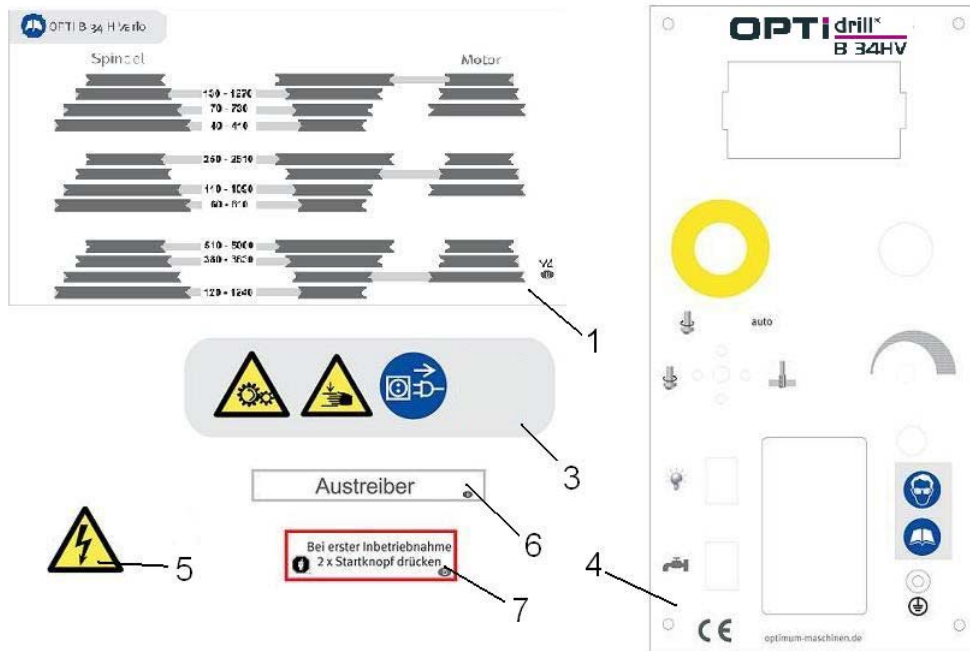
Maschinenschilder - Machine labels B34HV
